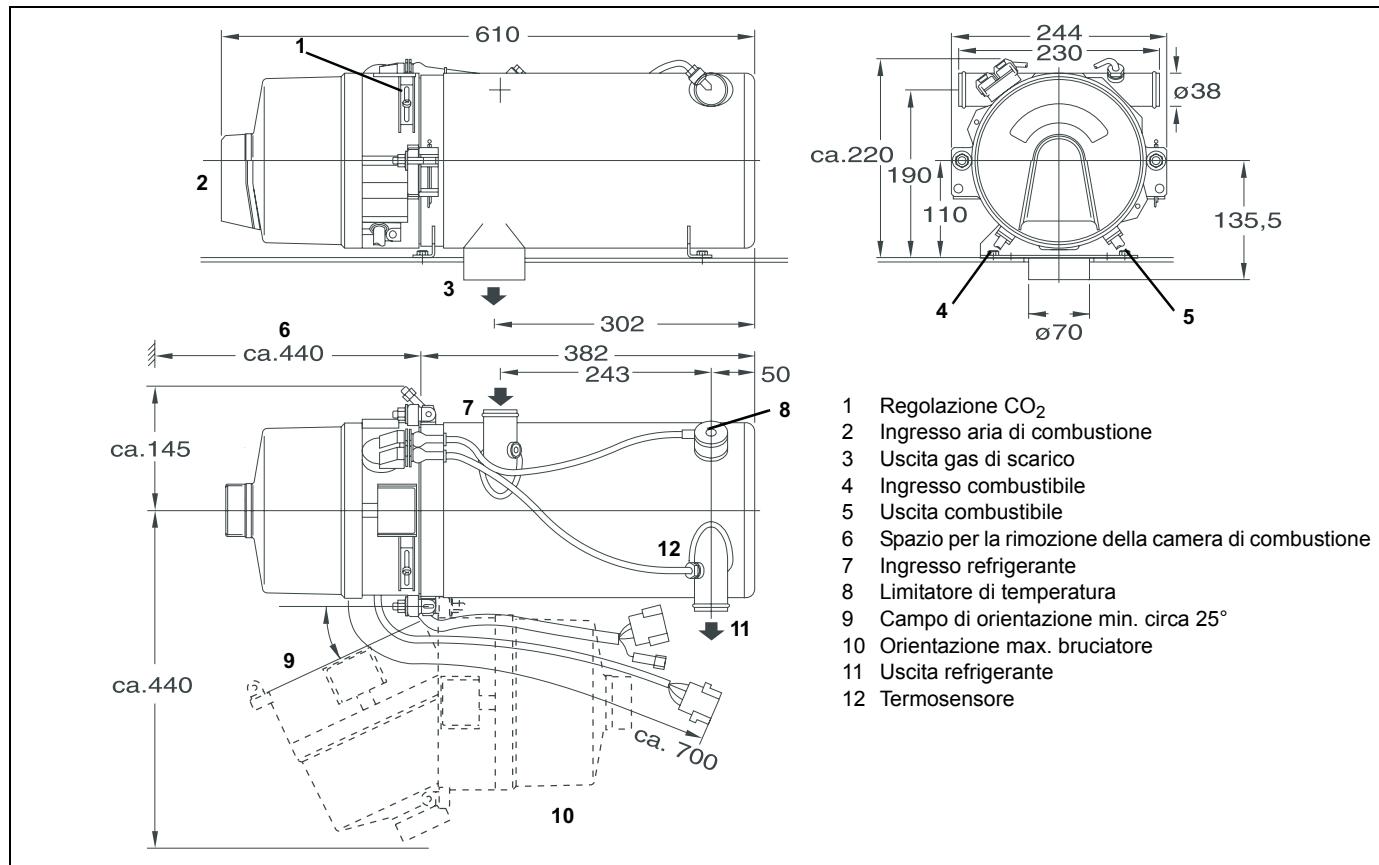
Dimensioni del riscaldatore Thermo 230 / 300 / 350 (montaggio orizzontale)
